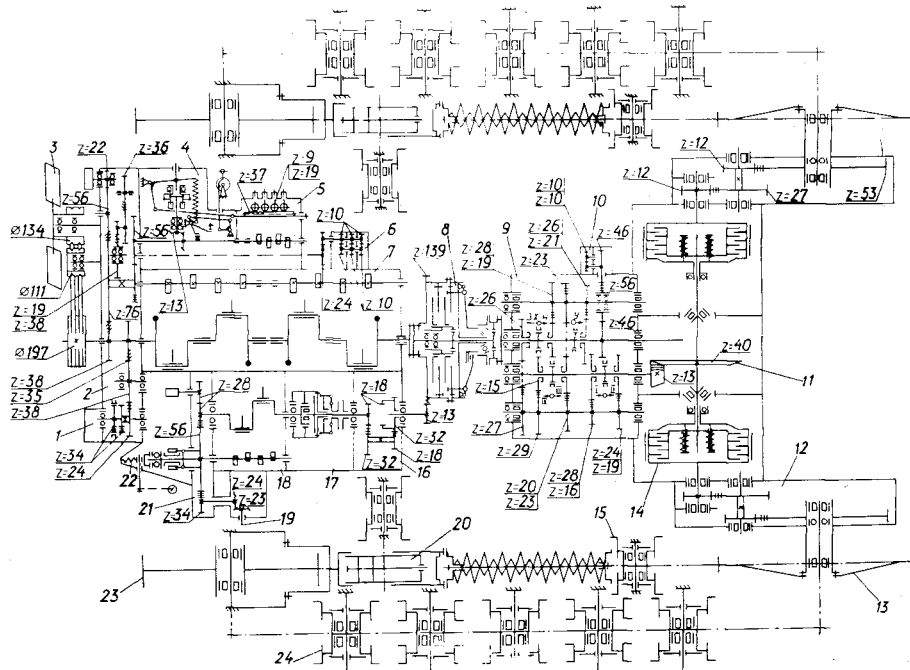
Кинематическая схема трактора с бортовыми редукторами с передаточным числом равным 9,94 и П-23У:
